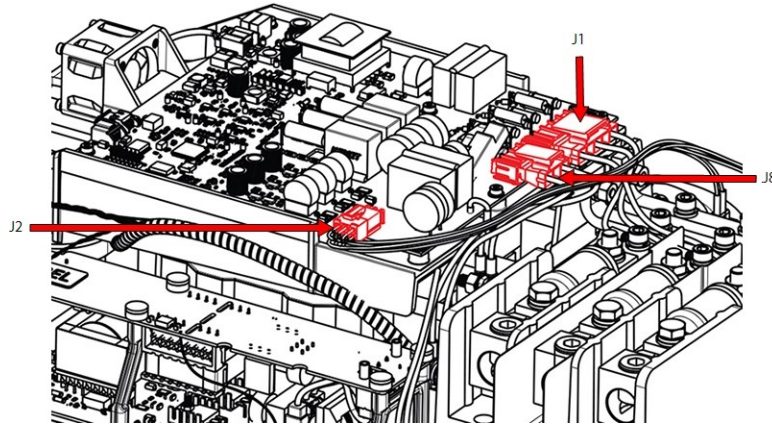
Desmontaje de J1 y J8 de arranque suave con cubierta abierta
